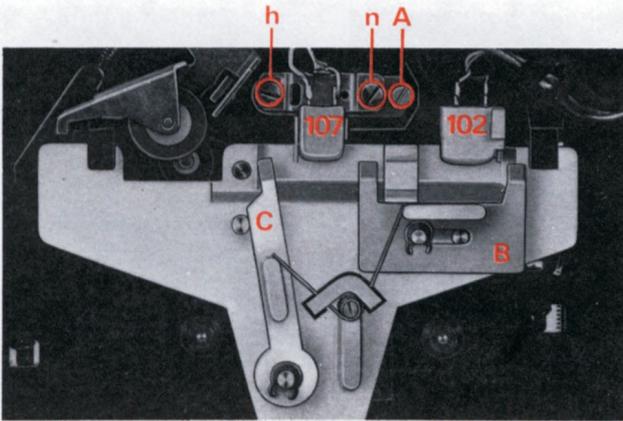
Einrichten des Kopfes mit Lehre 34000-029.00
